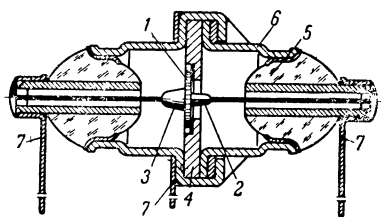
Устройство плоскостных триодов типов П1 и П2. 1 — германий; 2 — эмиттер (индий); 3 — коллектор (индий); 4 — держатель; 5 — стекланный изолятор; 6 — корпус; 7 — вывод.
